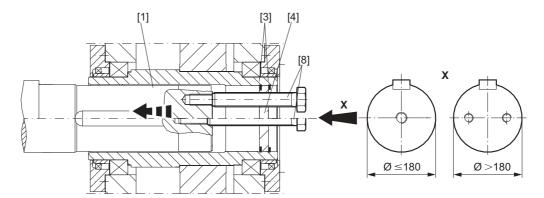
Desmontaje de reductores horizontales con unión por chaveta
